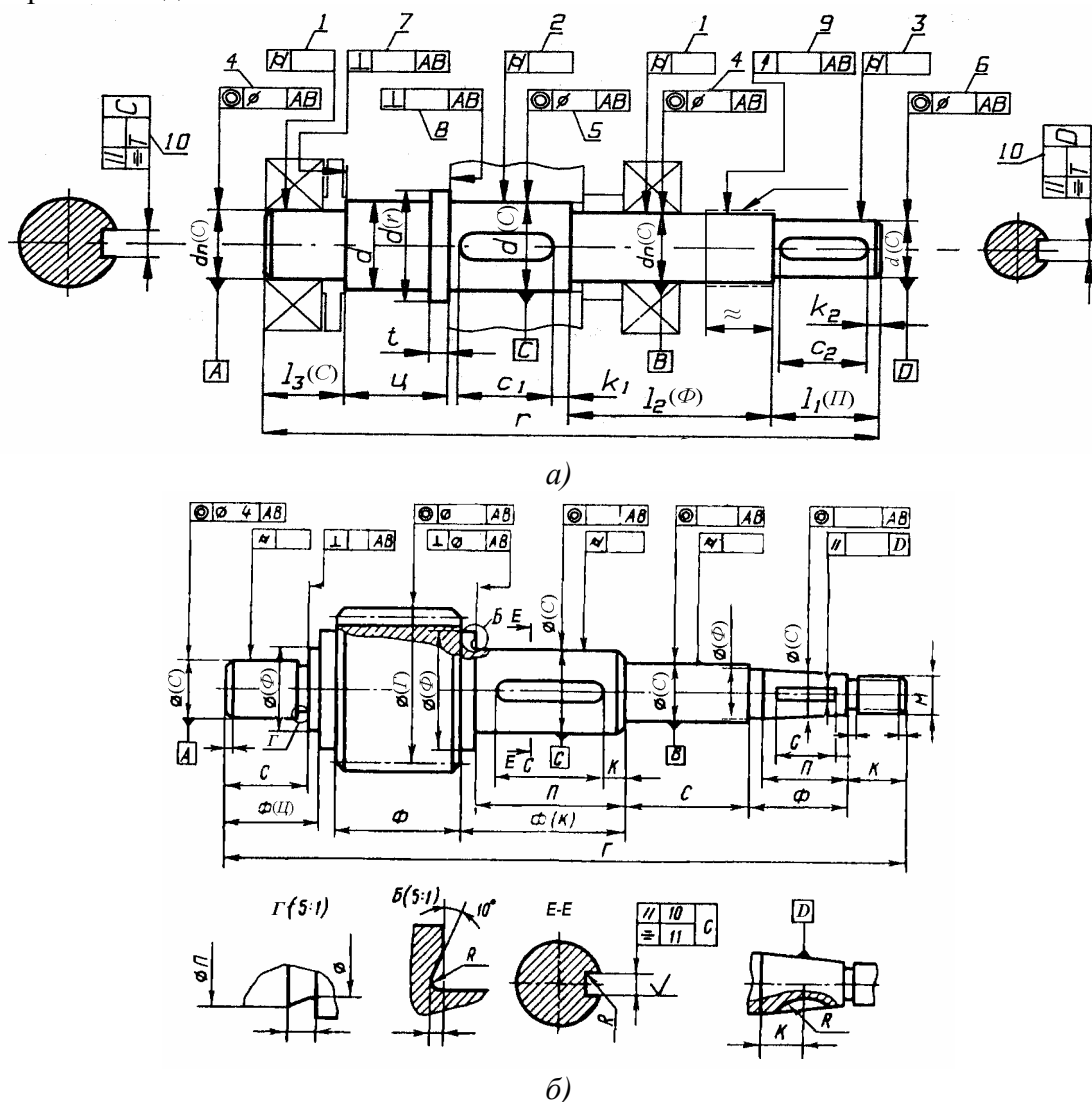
Изображение на чертеже вала – а и вала-шестерни – б: размеров, баз, допусков формы и расположения
